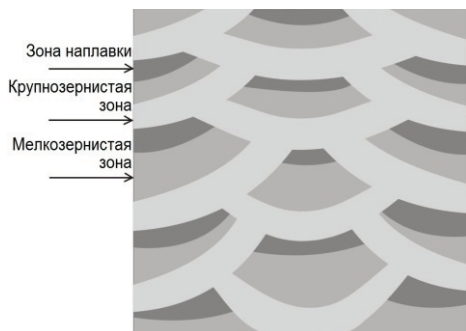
Представительный объем многопроходного сварного шва
